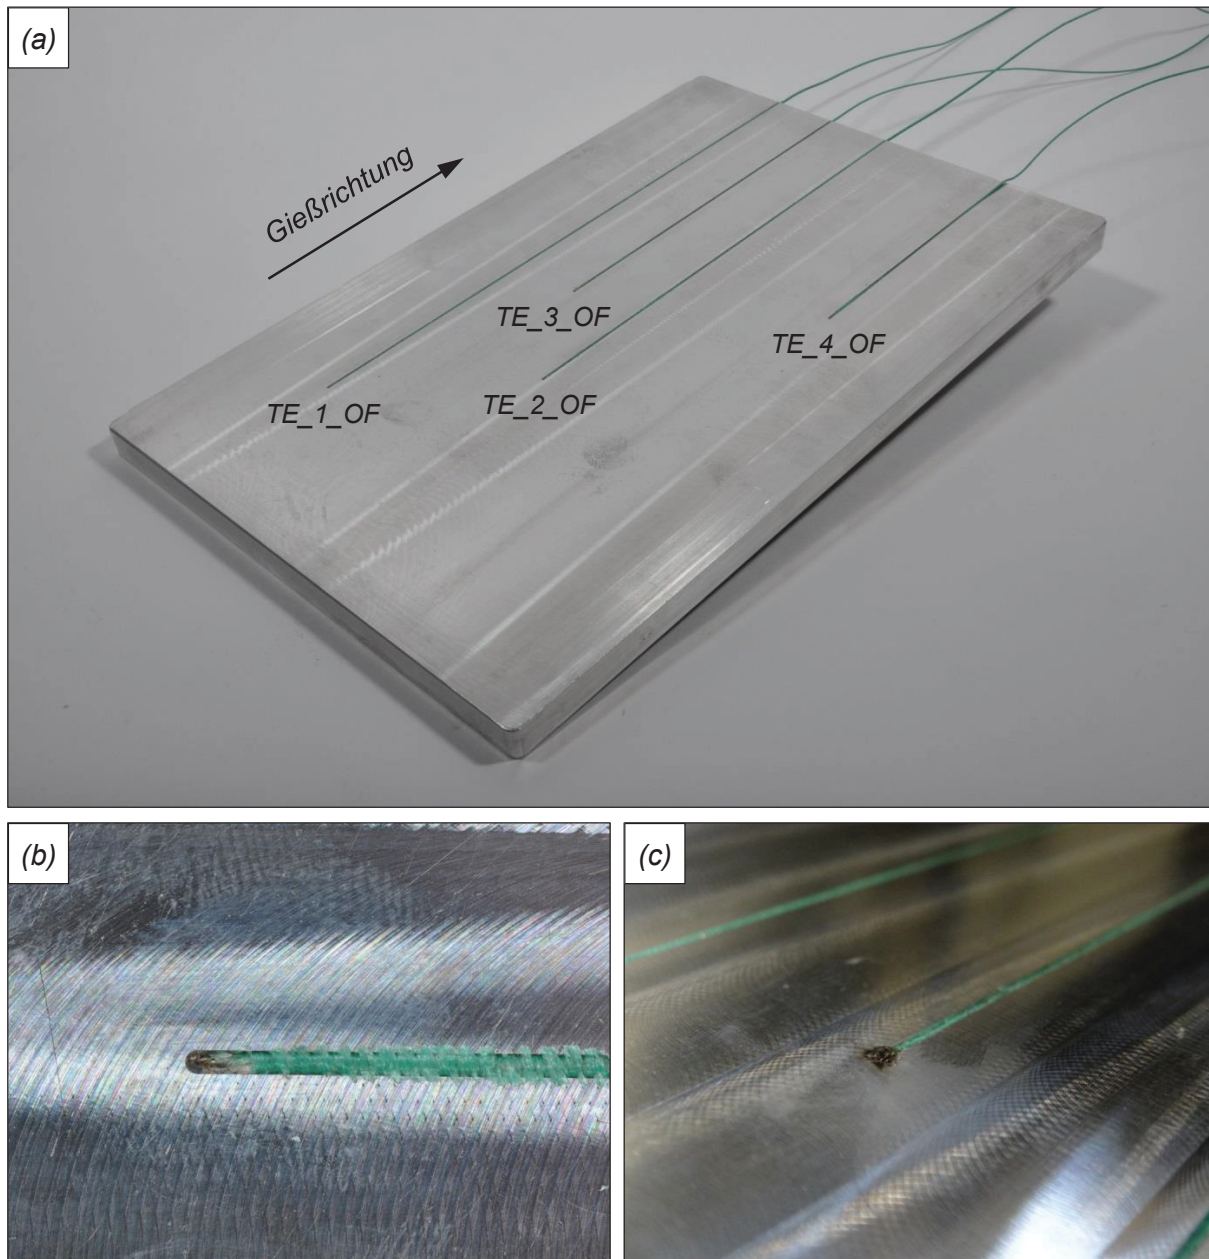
Übersicht der Substratplatte (a) mit eingelegten (b) und punktverschweißten (c) Thermodrähten für die Messung der Temperatur an der Substratoberfläche.
